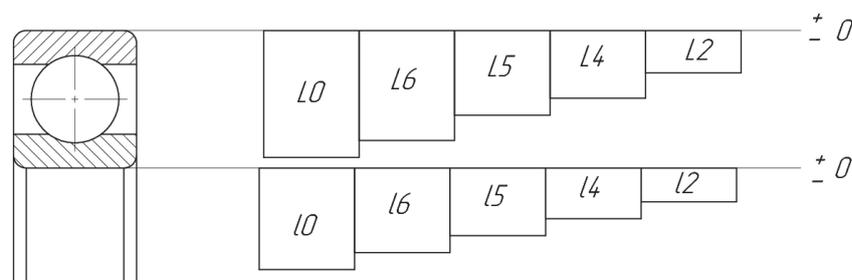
Схема расположения полей допусков на присоединительные размеры подшипников качения различных классов точности
